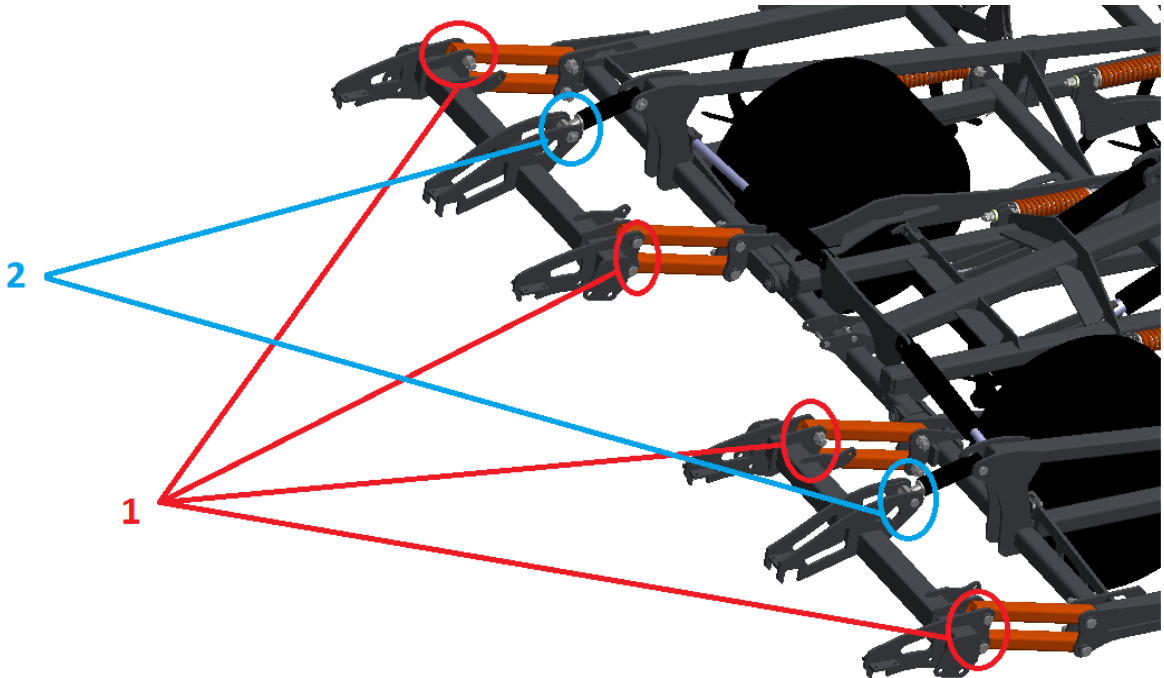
Montage der hinteren Befestigungsvorrichtung.
